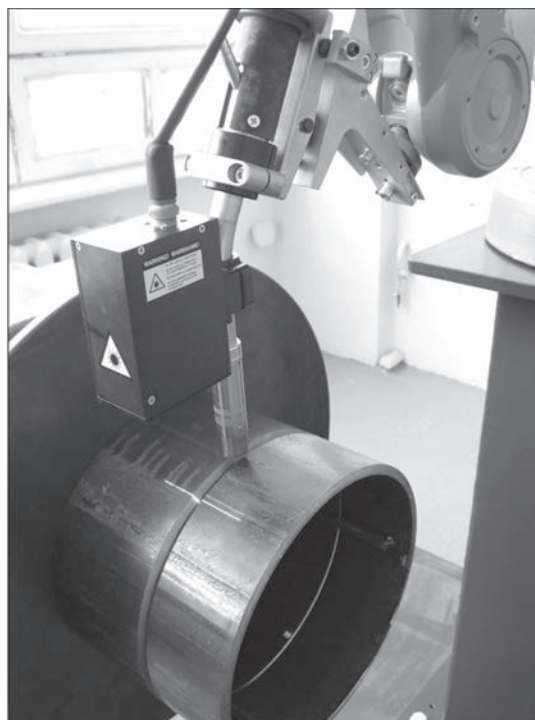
Сварочный робот с лазерным датчиком, разработанным в ИЭС
